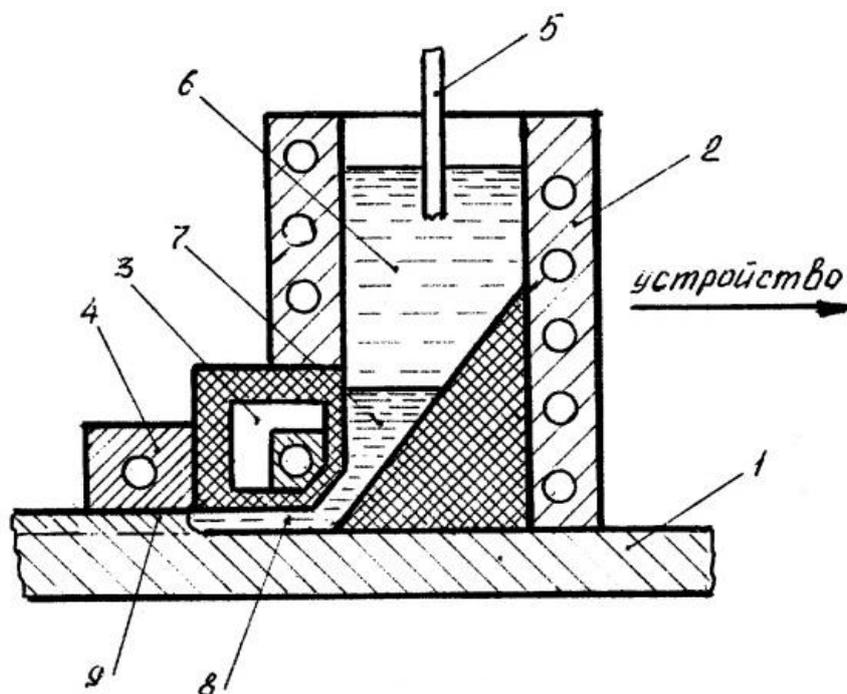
Устройство для ЭШН по патенту № 2093329: 1 – наплаваемый нож; 2 – кокиль; 3 – индуктор; 4 – охладитель; 5 – электрод; 6 – шлаковая ванна; 7 – ванна расплавленного присадочного материала; 8 – зазор; 9 – слой наплавленного материала.
